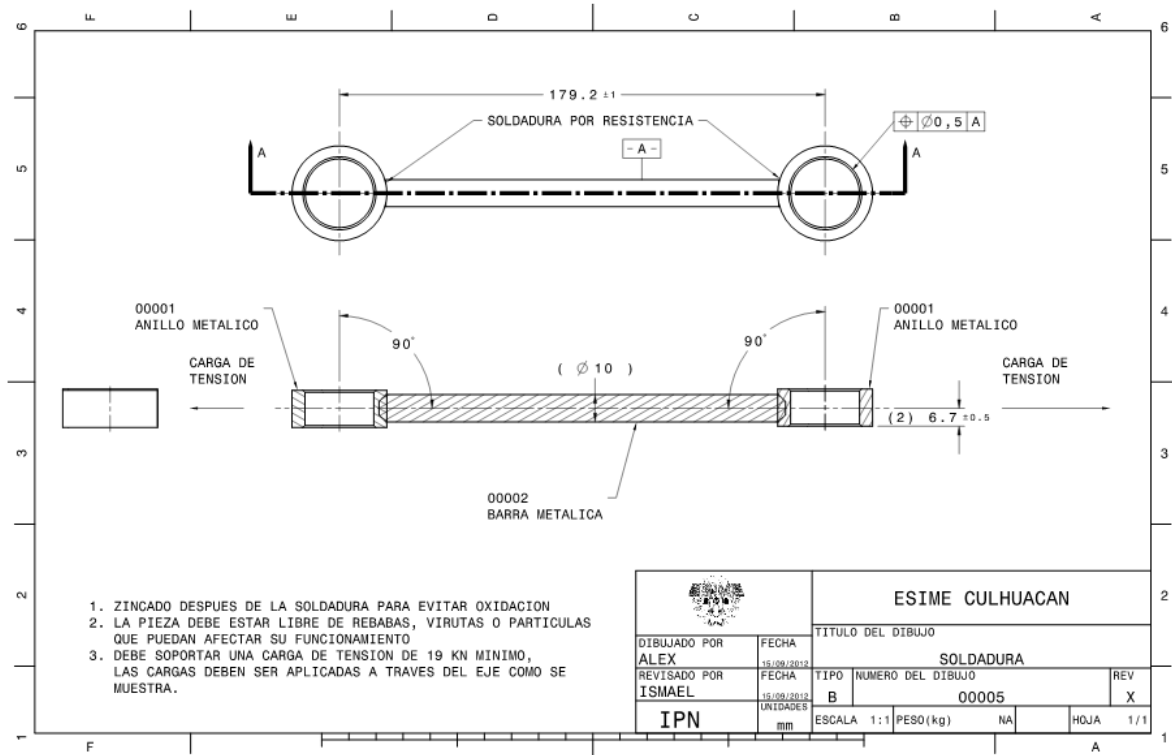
Plano de especificaciones de soldadura.
